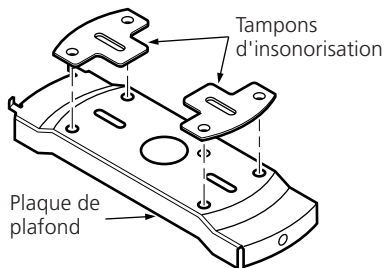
Placer les tampons d'insonorisation sur la plaque de plafond.
